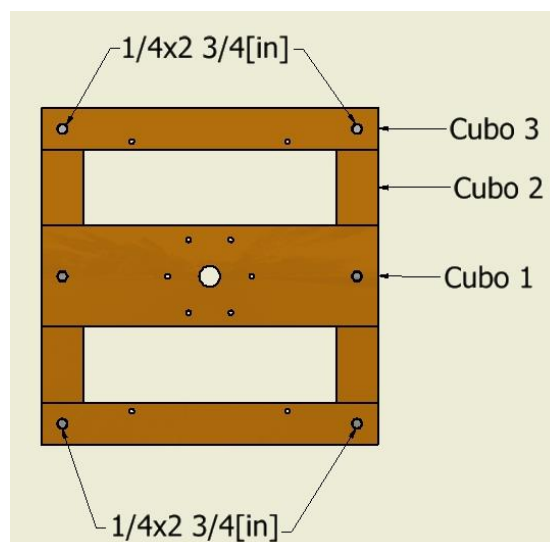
DIMENSIONES DE LA PARTE CUBO 2
